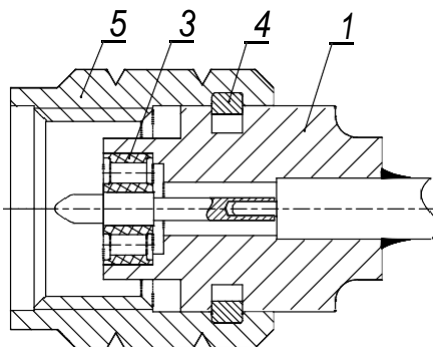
Установка накладной гайки на корпус кабельного соединителя
